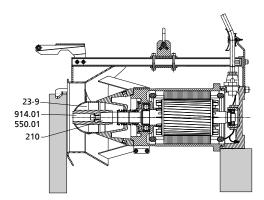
Desmontaje de la hélice en Amaline 300 con motor 86
